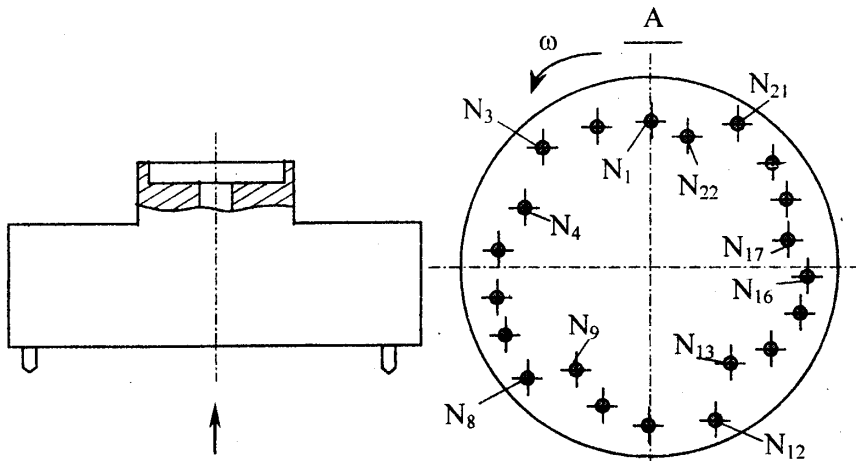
Розташування ножів на площині фрези (вид знизу; цифрами позначена нумерація ножів)
